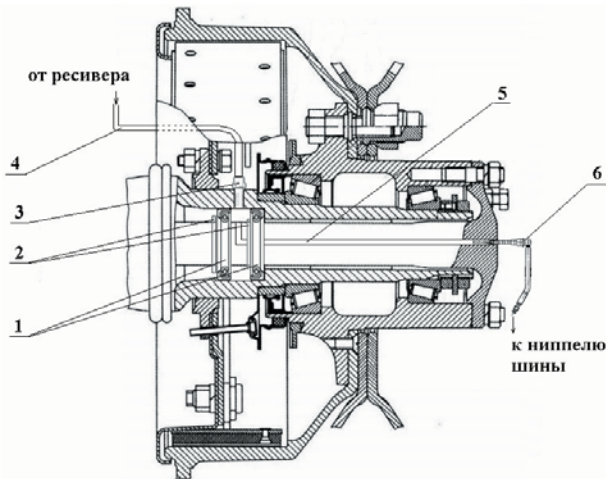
Ступица ведущего колеса автомобиля ЗИЛ-4331, оснащённого противобуксовочной системой:
